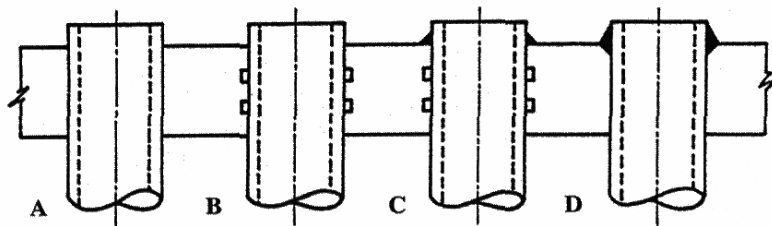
четыре типа соединения трубка – трубная доска. А – вальцовка, В – вальцовка с канавками, С – вальцовка с канавками и герметизирующей сваркой, D – сварка с высокой механической прочностью (без вальцовки и канавок).
